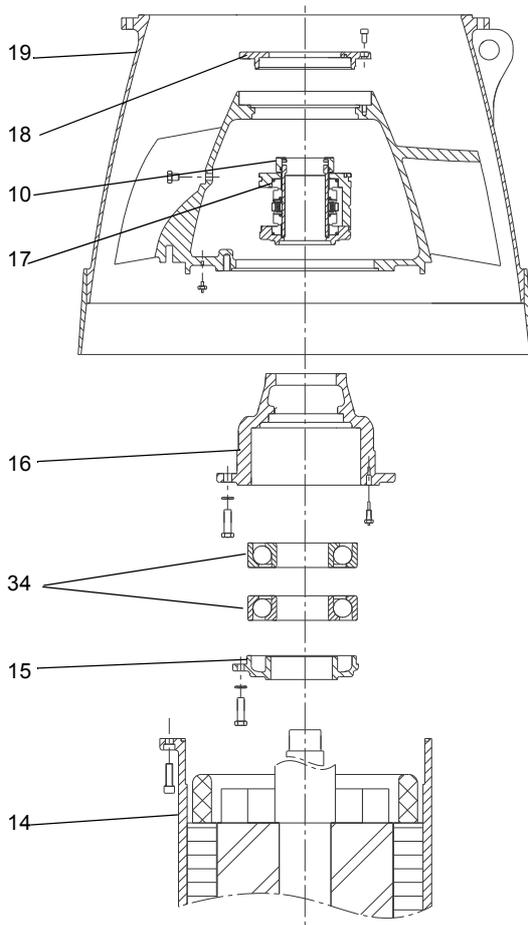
Габаритный чертеж, KPL 500-800 (нижняя часть).
